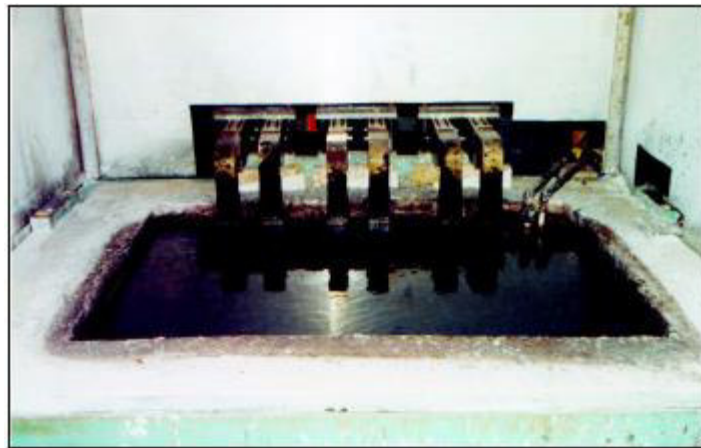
Proceso de soldadura por inmersión por el método de sal fundida.
